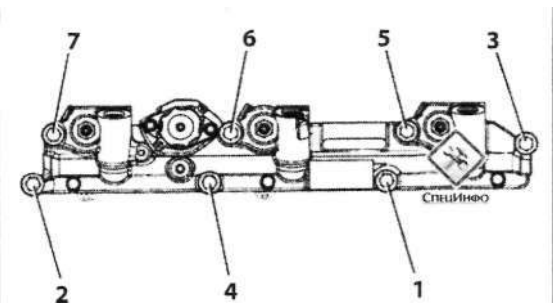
Порядок затяжки болтов крепления моторного тормоза «J».
